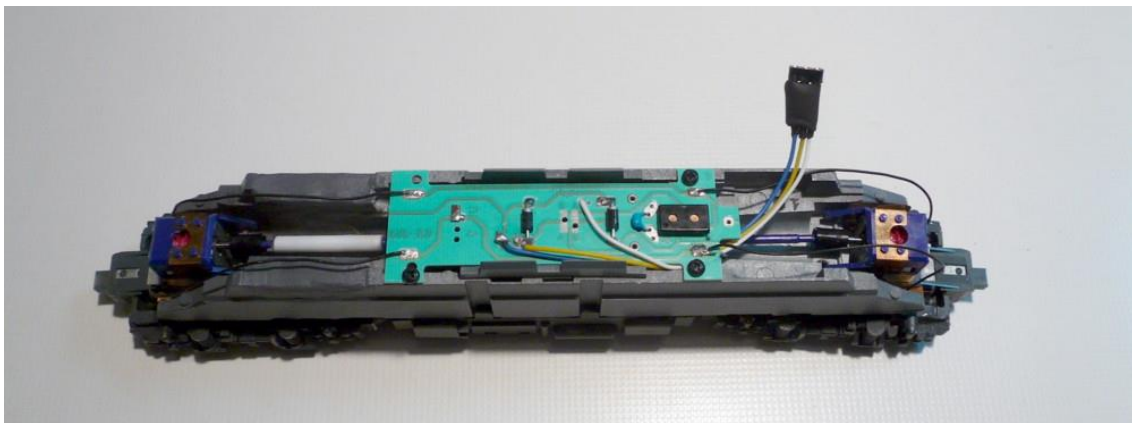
Sustitución de las bombillas por cables para conectar LEDs.
